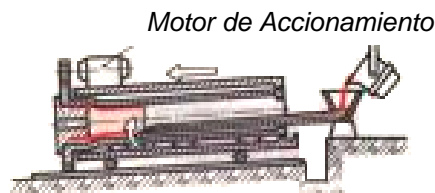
Fundición centrífugada – colada en moldes permanentes
